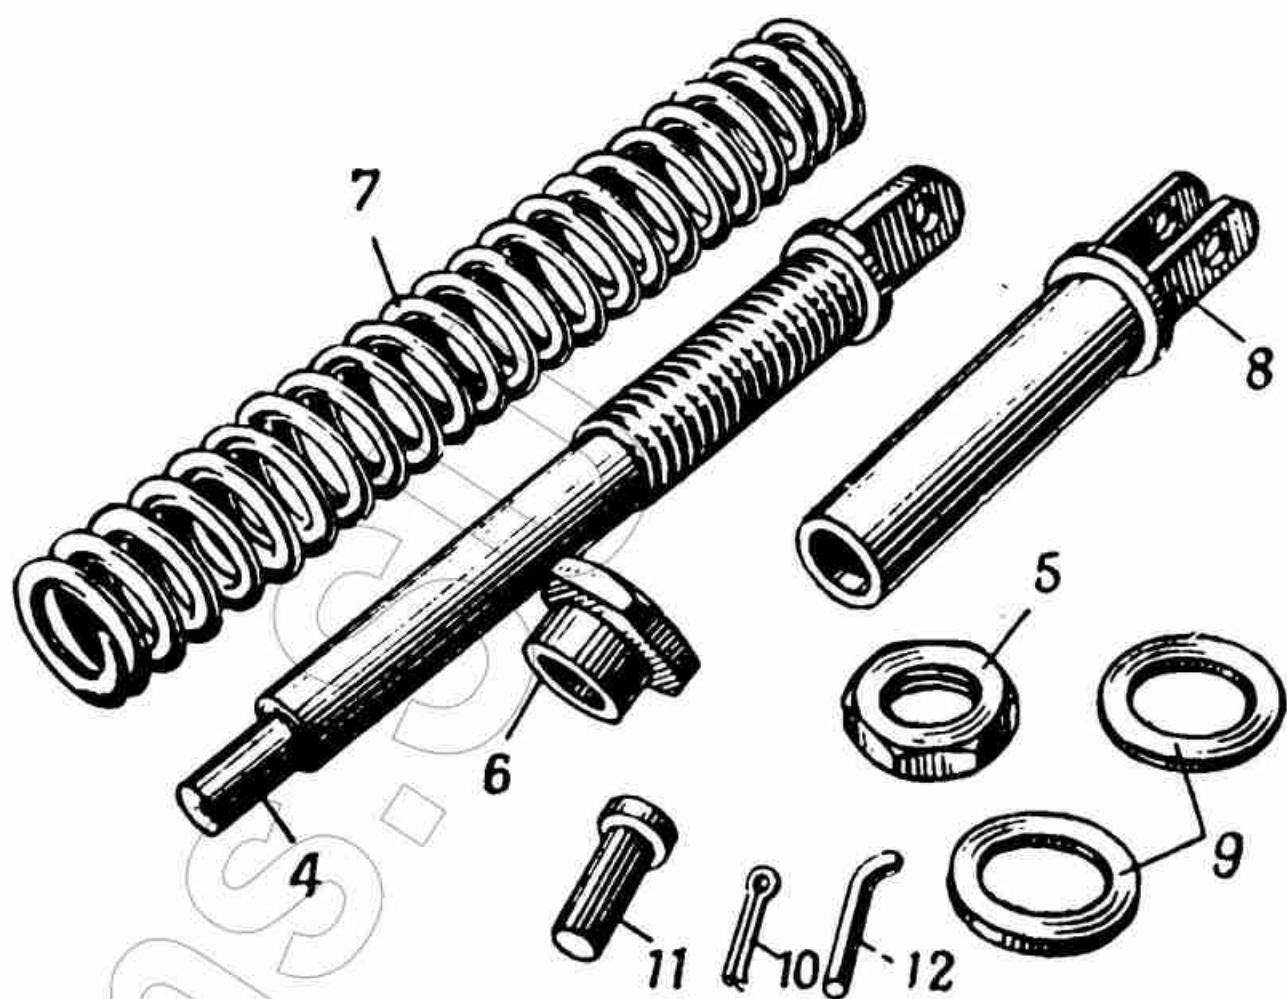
Детали компенсирующего механизма: 4 — стержень; 5 — гайка; 6 — нажимная гайка; 7 — пружина; 8 — вилка; 9 — шайбы; 10 — шплинт; 11 — ось; 12 — чека
